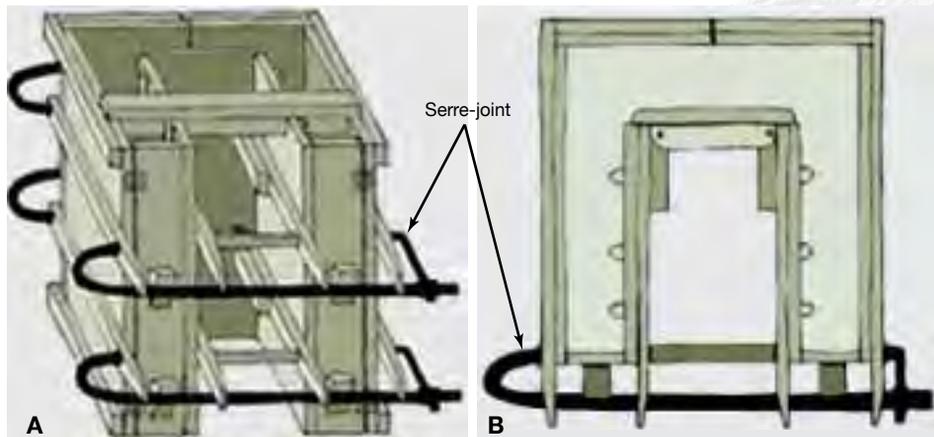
Moule de moine. A : Vue de face ; B : Vue de dessus.
